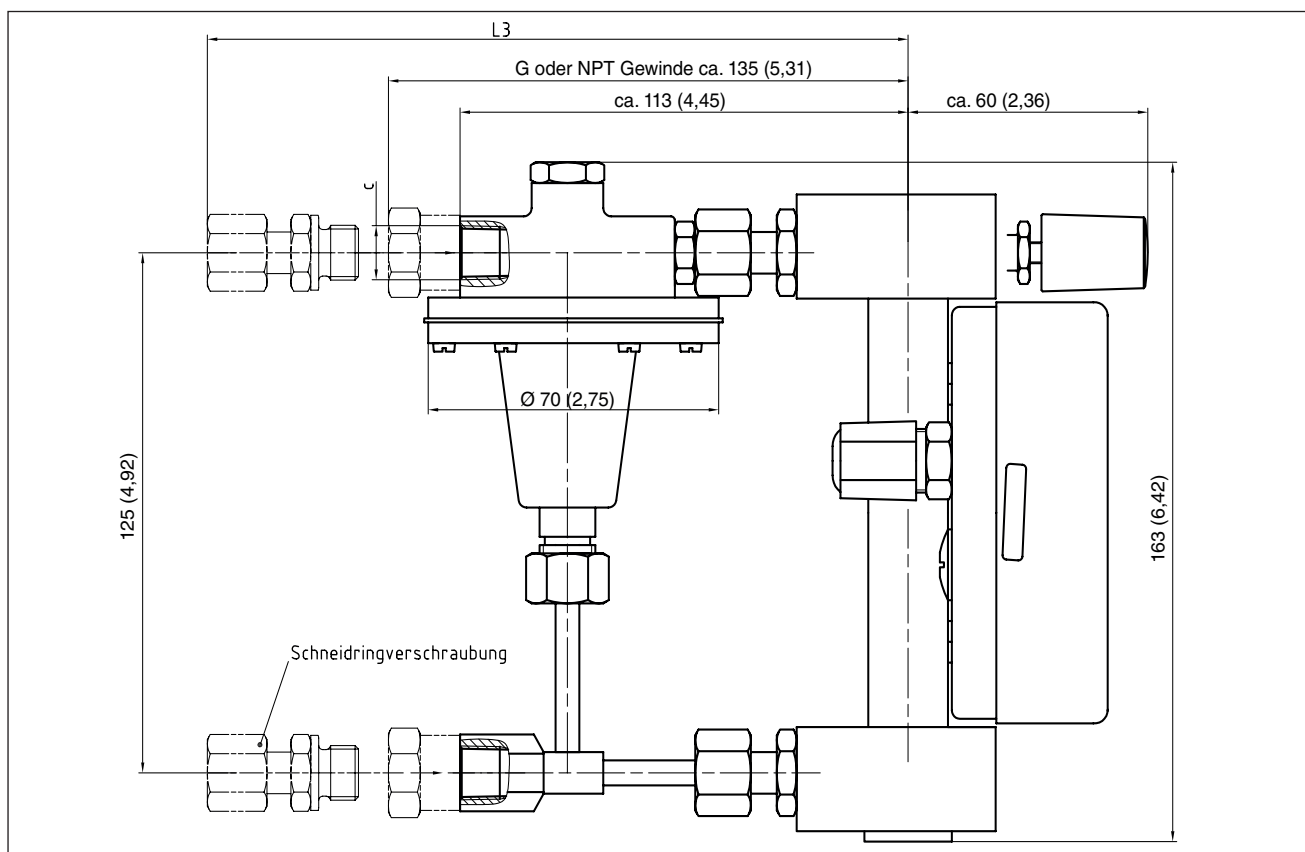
Ausführung mit Ventil im Ausgang und Gegendruckregler, Abmessungen in mm (Zoll)
